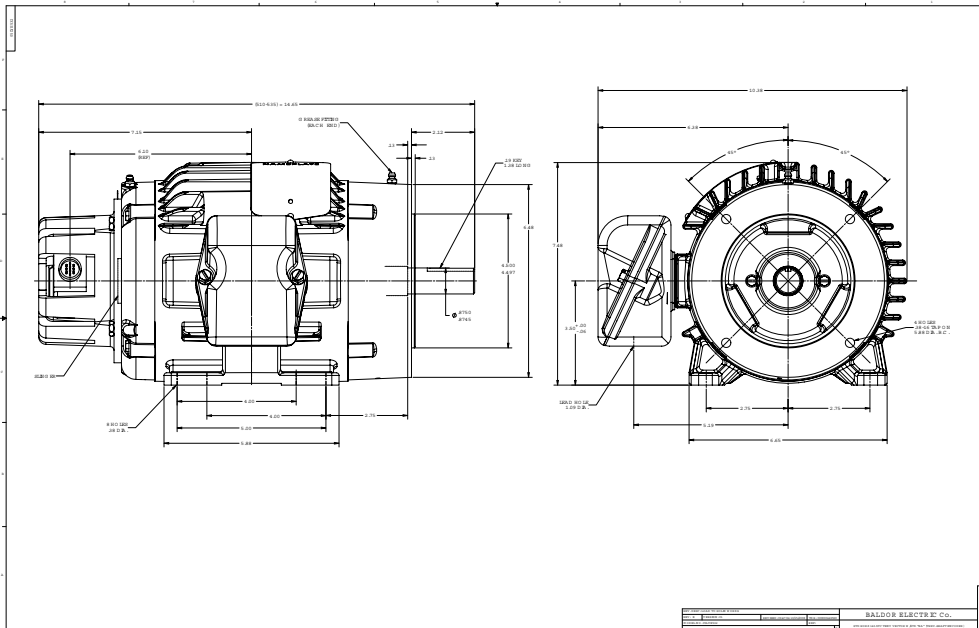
Diseño mecánico y dimensiones del motor de inducción
